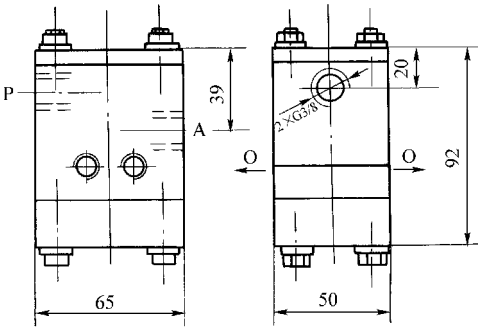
FQ0803 型二位三通延时换向阀外形尺寸
